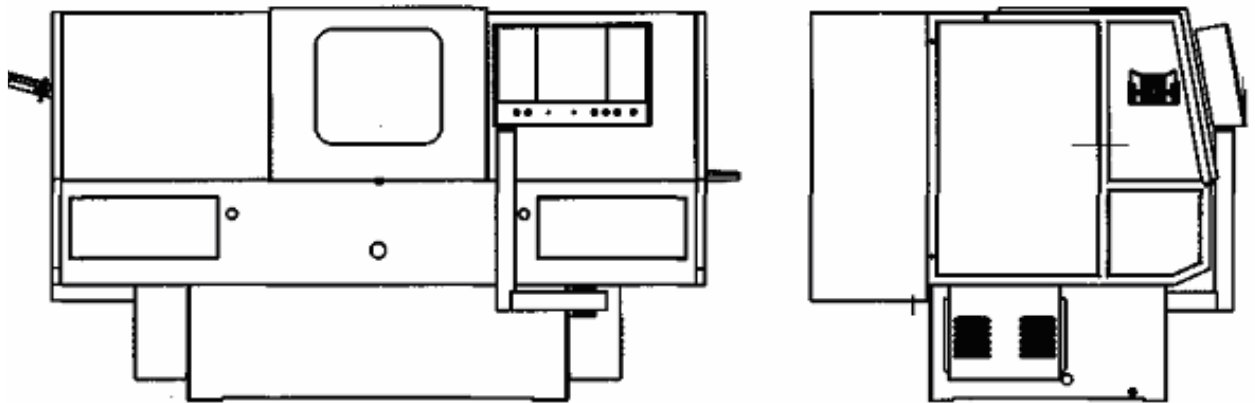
Загальний вигляд двошпиндельного токарного верстата з ЧПК.
